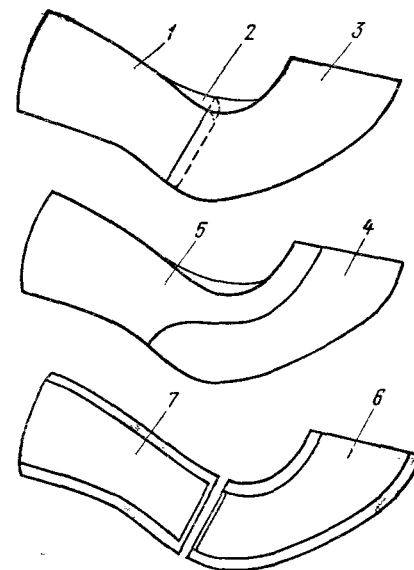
Схема сборки заготовки верха туфель-лодочек с отрезной союзкой
